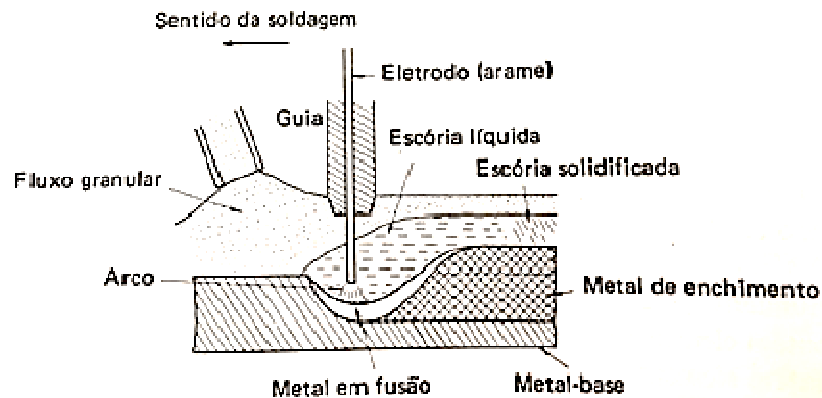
Soldagem a Arco Submerso (Esquemático).
